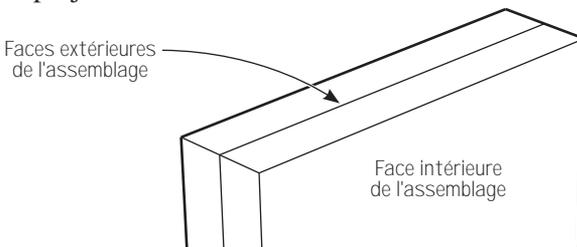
Placer les planches face contre face, soigneusement alignées pour le traçage. Il est conseillé de les serrer ensemble pour éviter qu’elles bougent.
